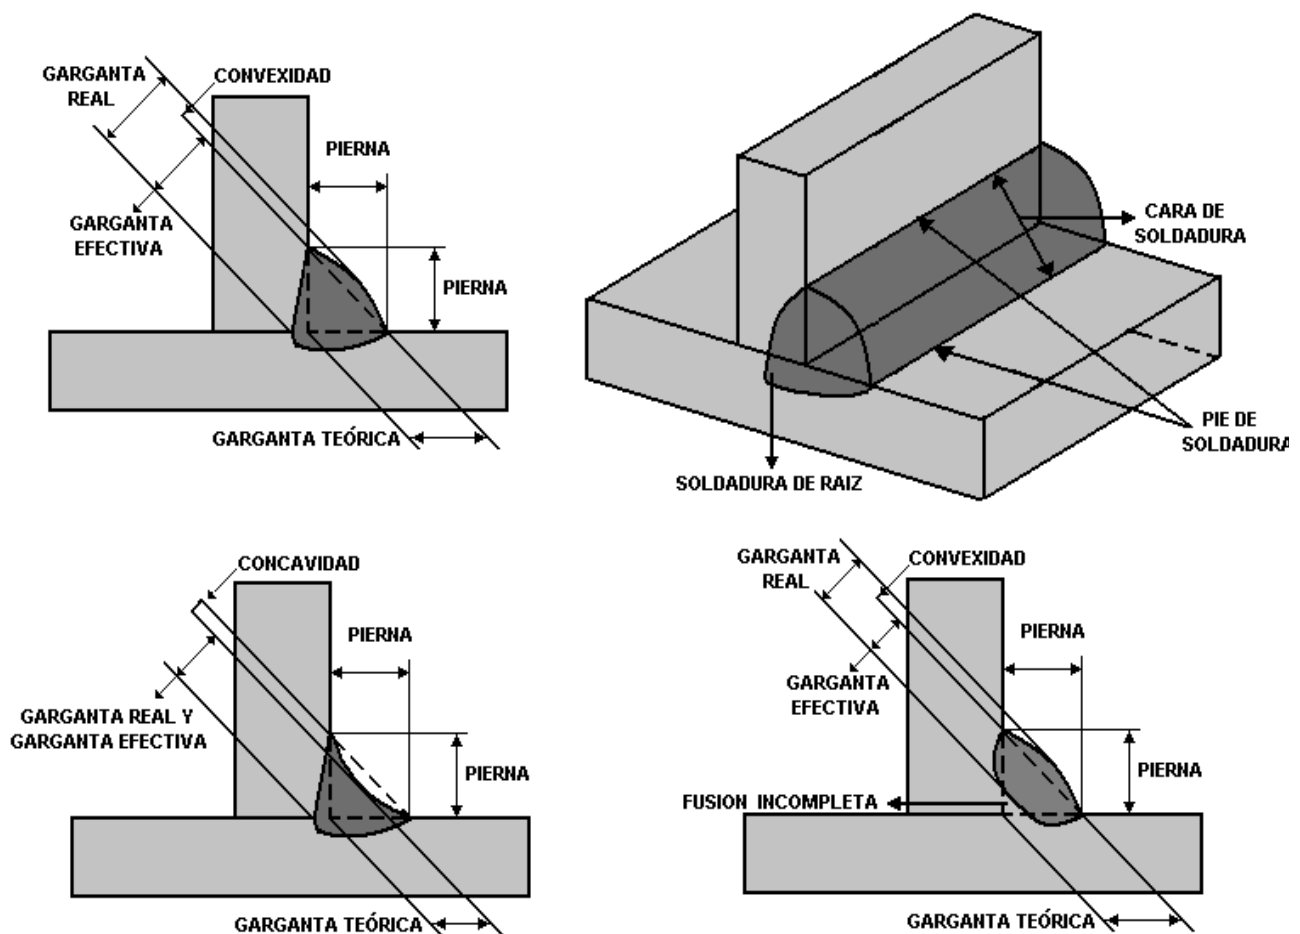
Partes de una soldadura en filete (7, 8, 18, 30)
